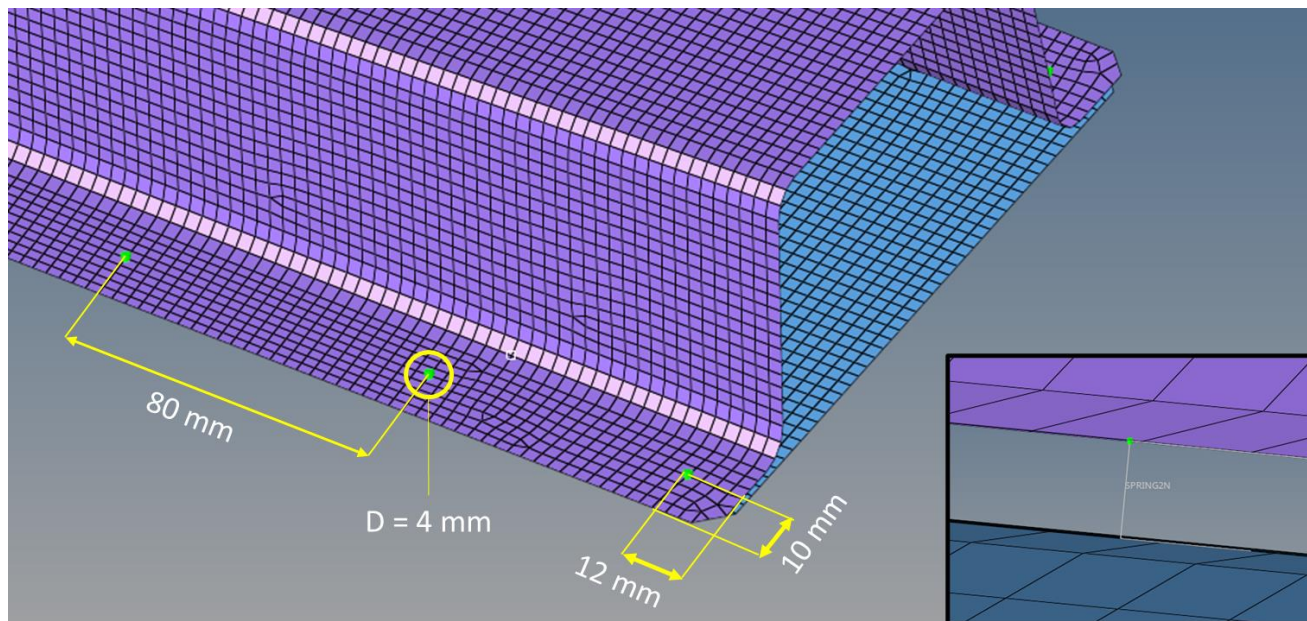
Especificaciones de los puntos de soldadura utilizados en el modelo de elemento finito.
